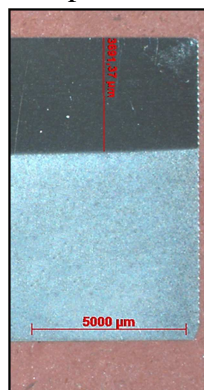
Espessura de 3,69137 mm de revestimento de Inconel 625, do fabricante Butting. (CENPES TMEC).
